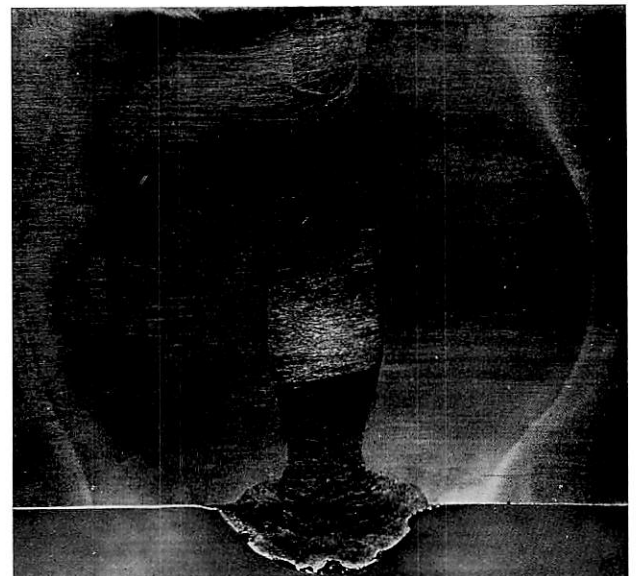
Zwischengußschweißung mit Stauchung,
